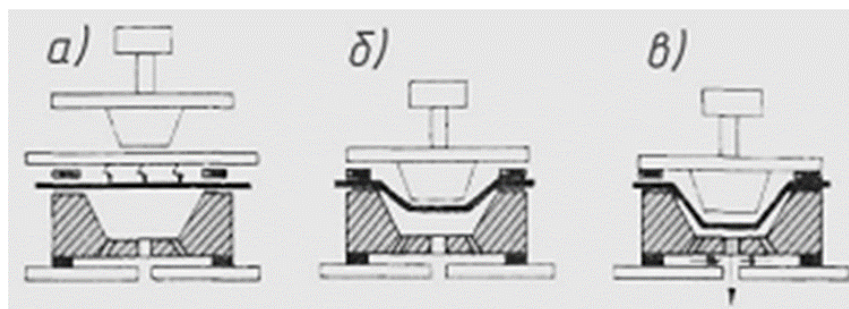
Схема негативного формування з попередньою механічною витяжкою
